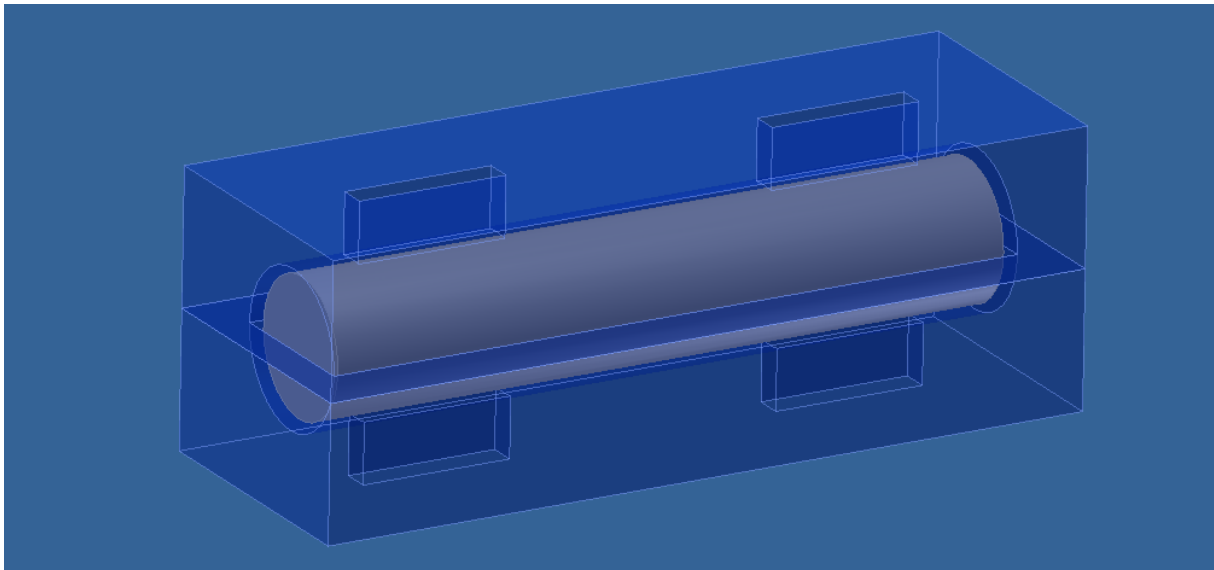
Saugwerkzeug mit wellenförmigem Bauteil und Luftspalt
